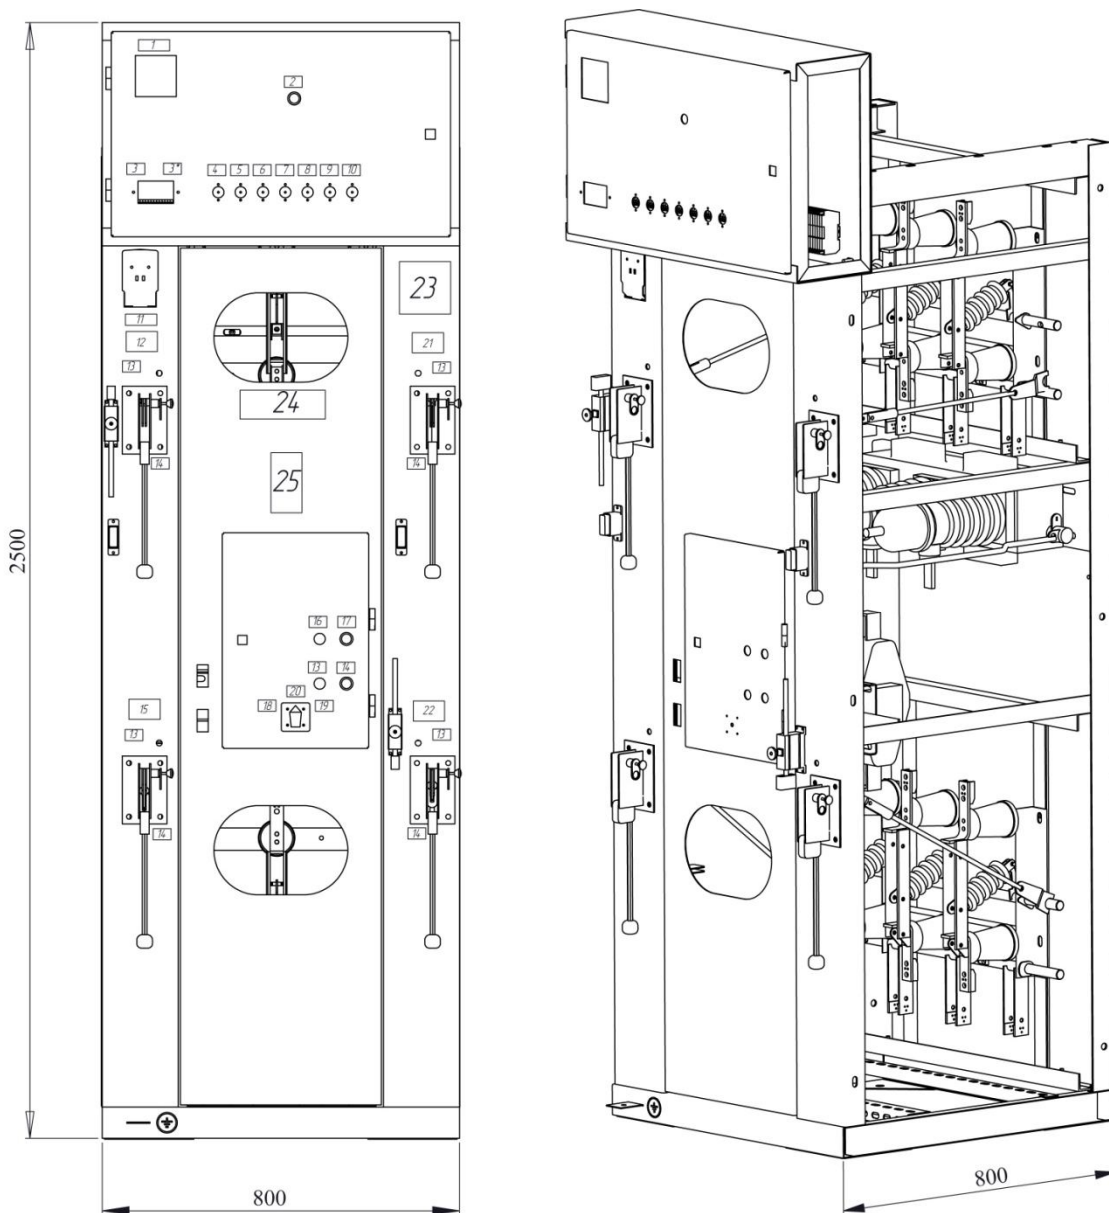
Внешний вид, габаритные размеры камер КСО393М с вакуумным выключателем ВВ/TEL
